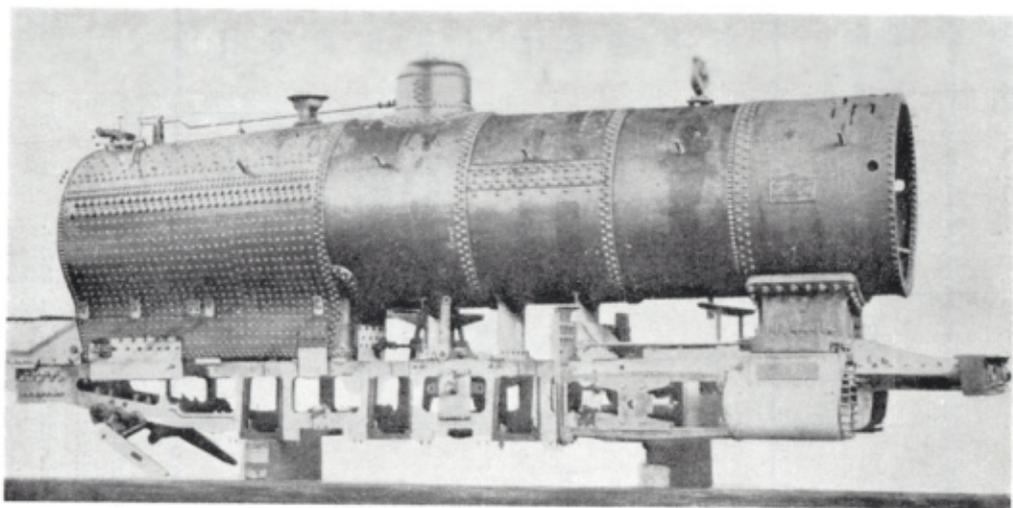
Châssis et chaudière de la n° 151 du BESSEMER RR.
